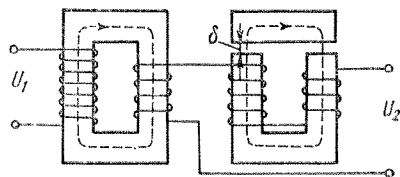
Сварочный трансформатор с реактивной катушкой
